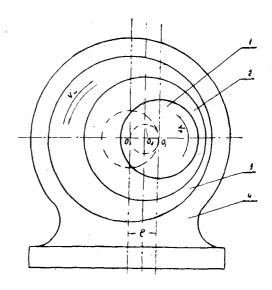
Схема приспособления с двумя эксцентричными втулками.
